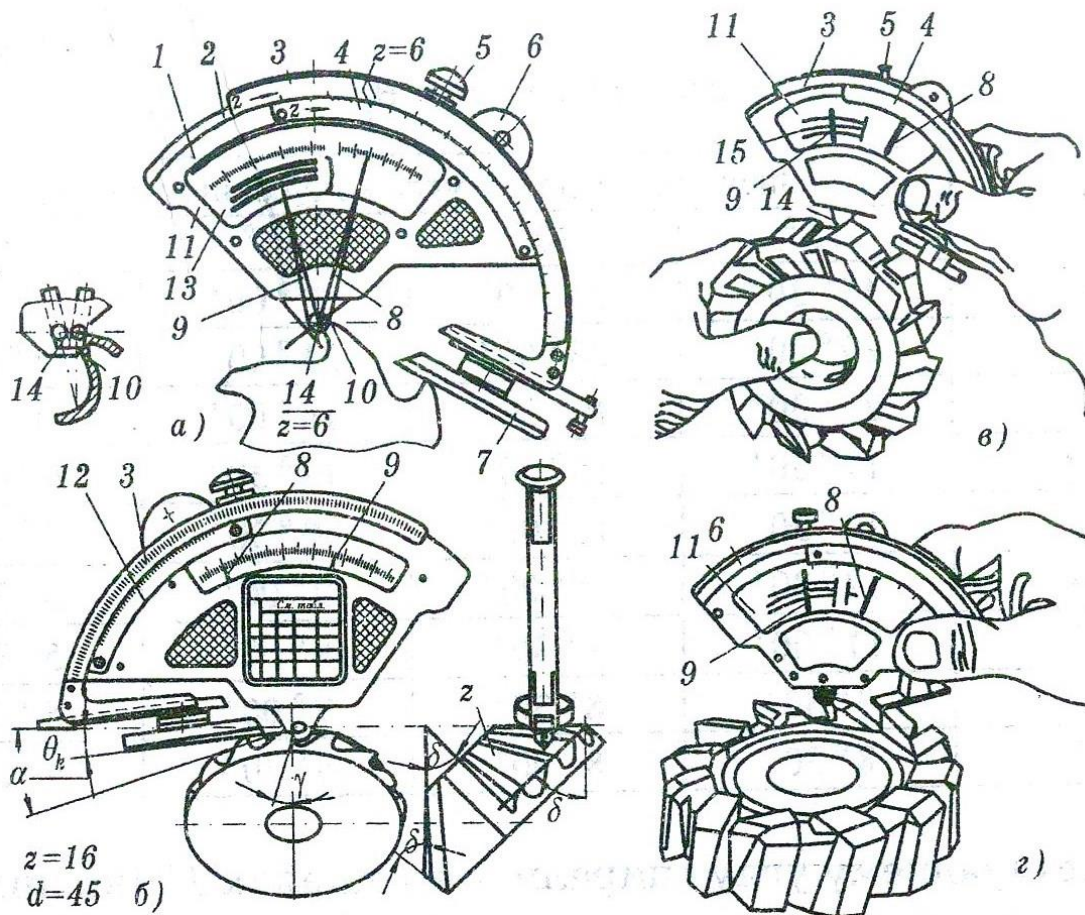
Самоустанавливающийся угломер конструкции Неприна: а - измерение углов заточки зубьев по цилиндру; б - измерение углов заточки зубьев по конусу; в - измерение углов заточки зубьев на цилиндрических поверхностях; г - измерение углов заточки зубьев на торцовых поверхностях: 1 - корпус; 2 - направляющая; 3 - движок; 4, 11, 12 и 13 - шкалы; 5 - стопор; 6 - тормоз; 7 - опорная линейка; 8 и 9 - стрелки; 10 - ось; 14 - измерительный шарнир; 15 - шкала
